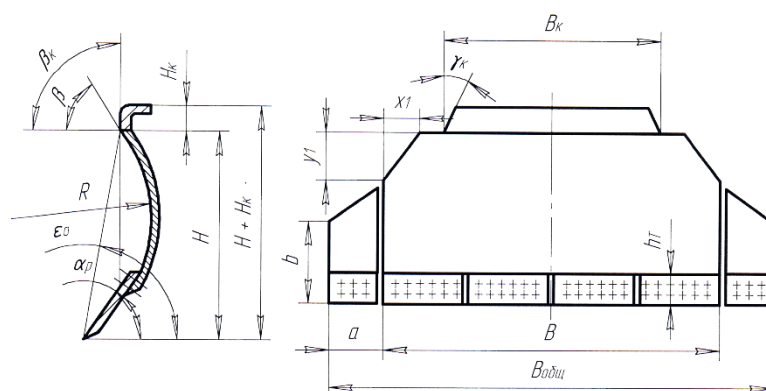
Схема бульдозерного отвала с боковыми скосами и ножами-уширителями
